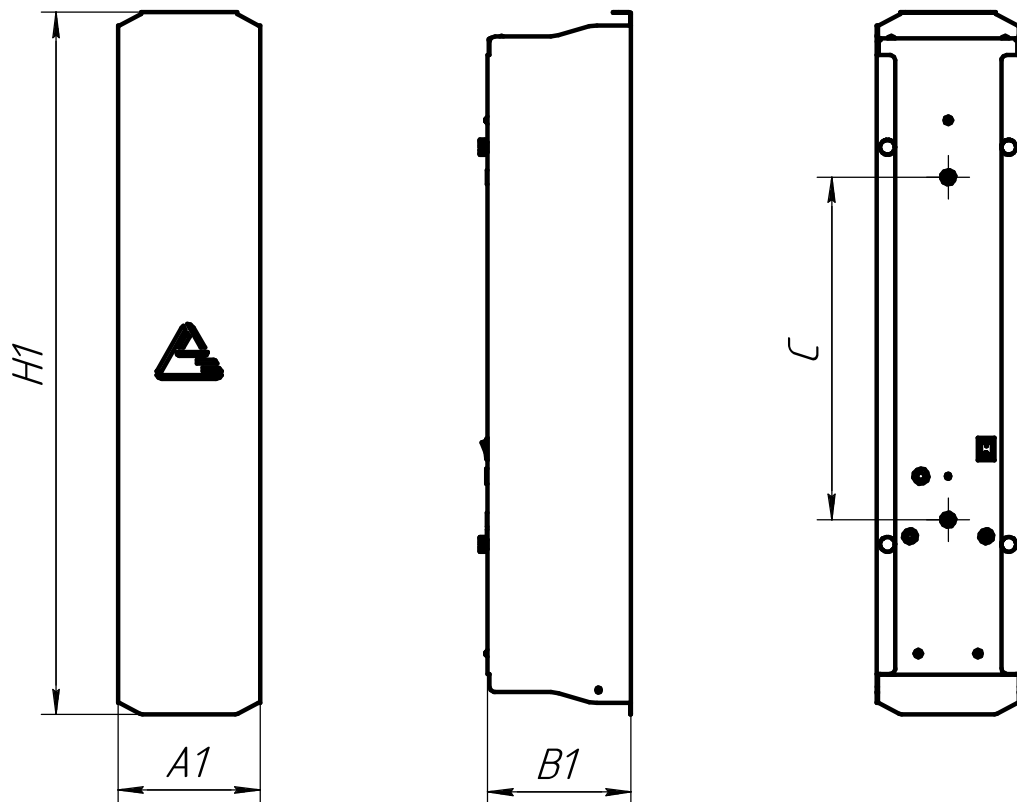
габаритные размеры рециркулятора без опоры.
